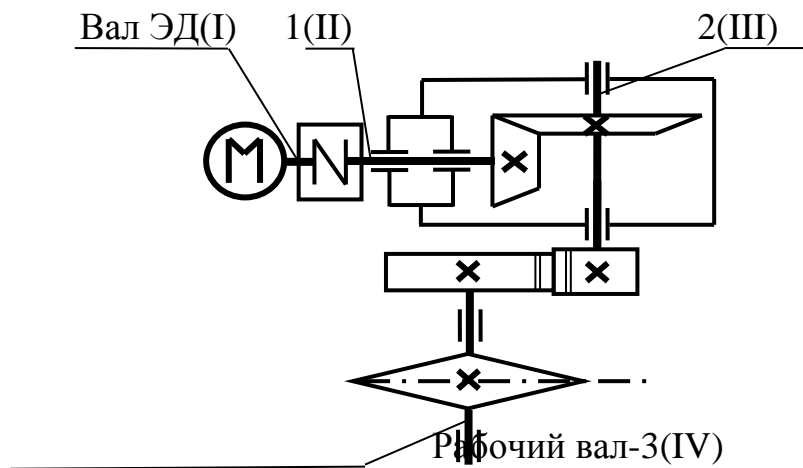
Образец схемы привода с открытой цилиндрической передачей
